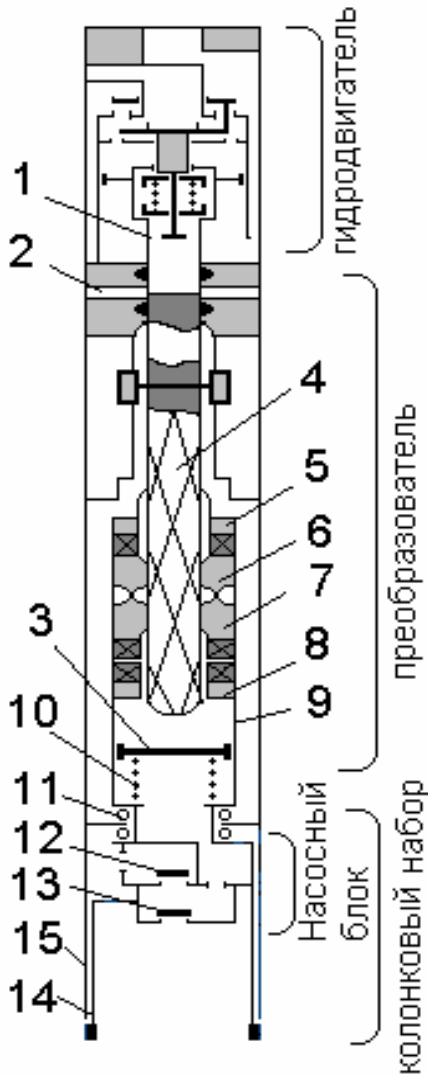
Схема гидробура с универсальным винтовым преобразователем
